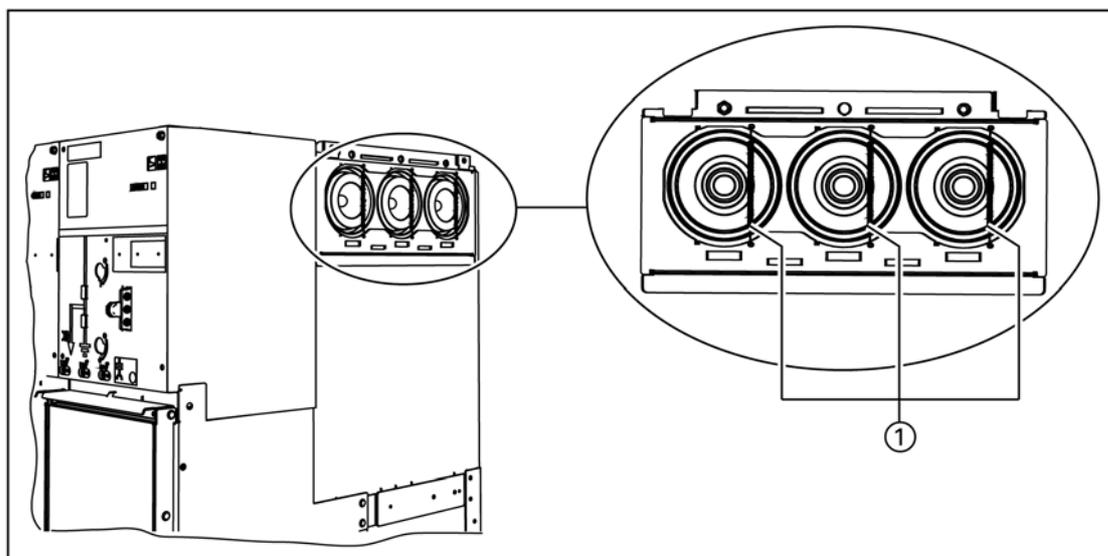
Правое соединение сборной шины с заземляющими контактными пружинами
